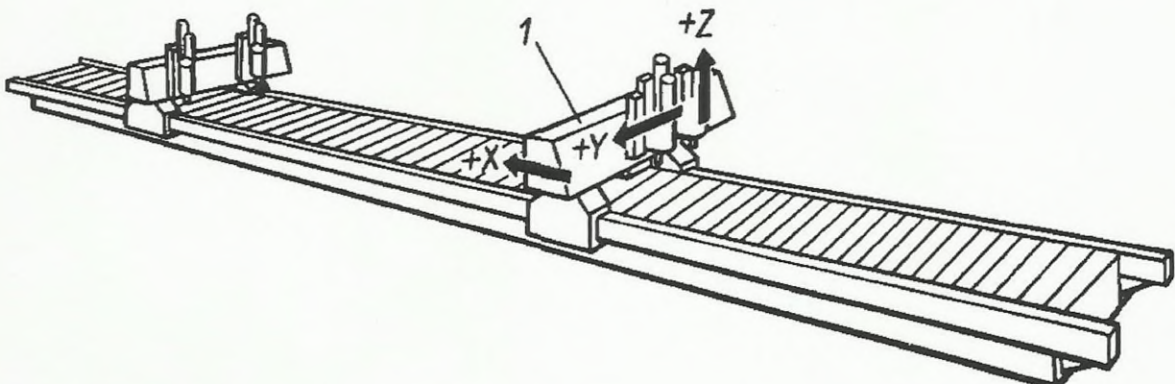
Типова компоновка порталних фрезерних верстатів з рухомими порталами
